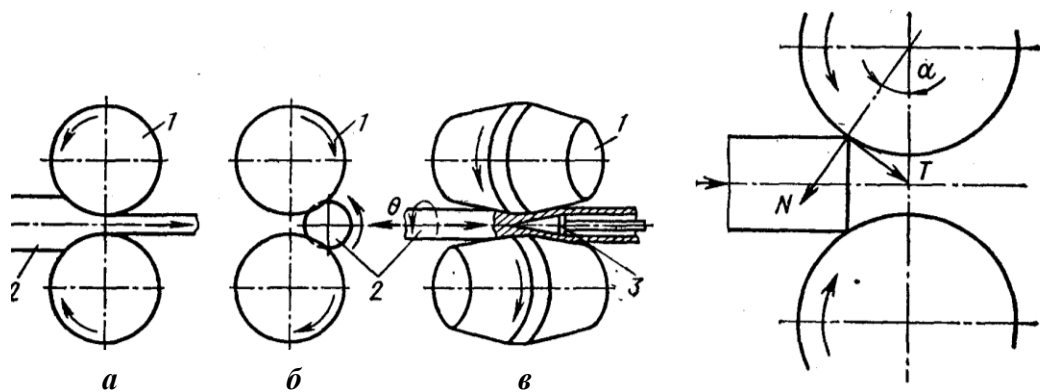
Виды прокатки и схема действия сил в момент захвата заготовки валками
